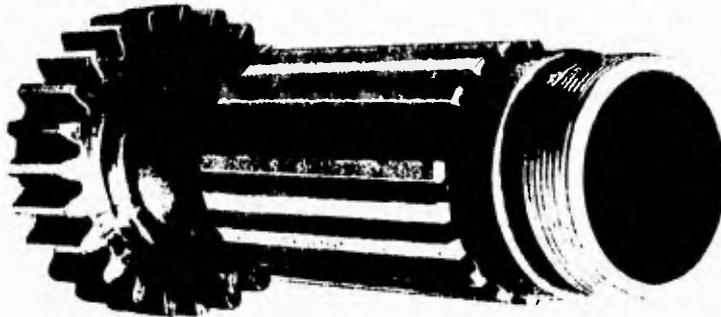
Grietas por esmerilado, en un engranaje.
